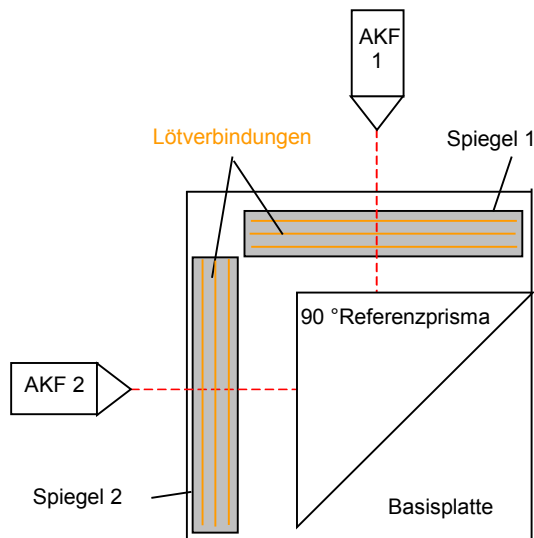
Versuchsaufbau zur Montage der Spiegelbaugruppen
